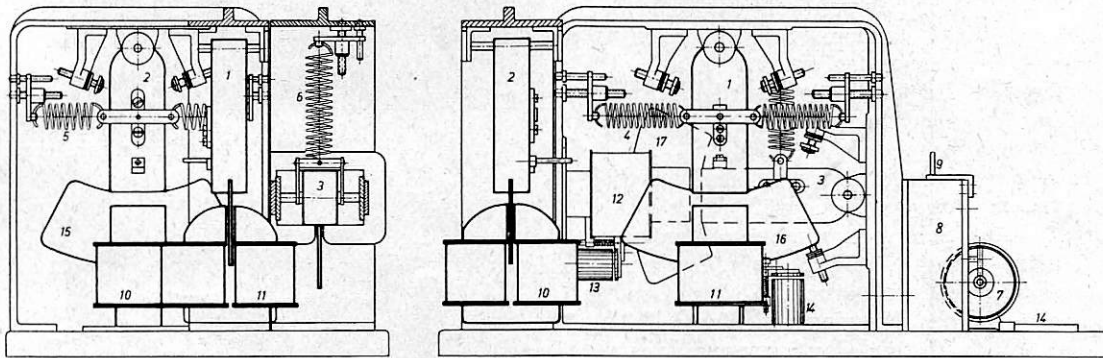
Dreirichtungsschwingungsmesser mit Wirbelstromdämpfung.
